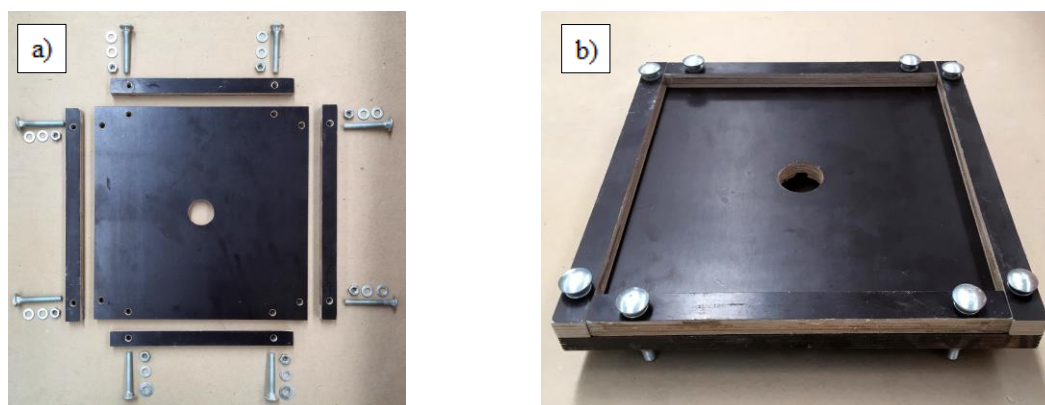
Molde utilizado no fabrico dos provetes: a) Componentes do molde; b) Molde montado.
